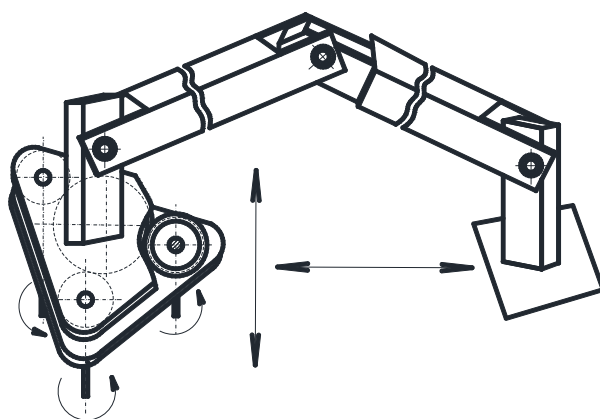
Манипулятор для выполнения отверстий и закрепления обломков строительных конструкций
